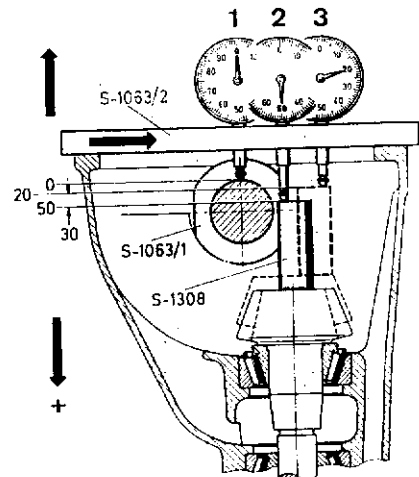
Réglage de la hauteur du pignon d'attaque
